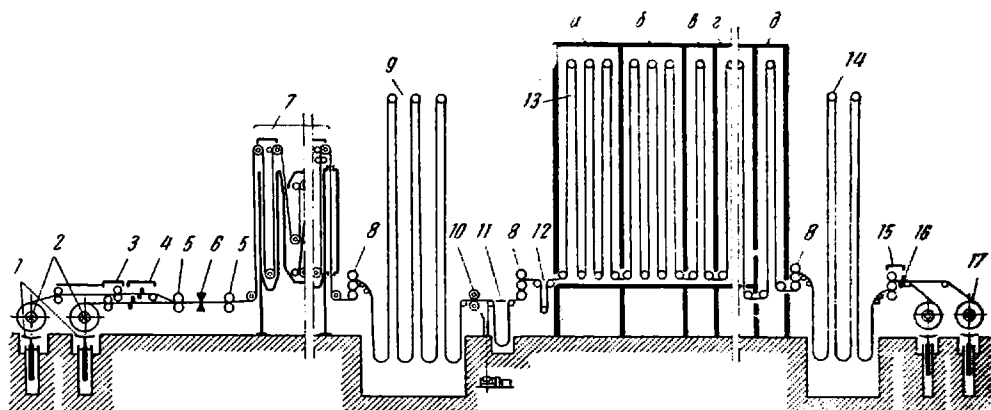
Агрегат непрерывного отжига листовой стали с башенными печами
